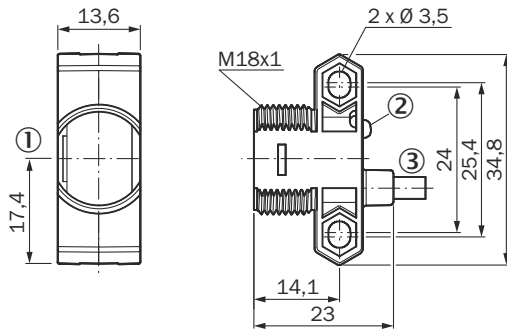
ZSE18-1xxxxx/ZSE18-Axxxxx
